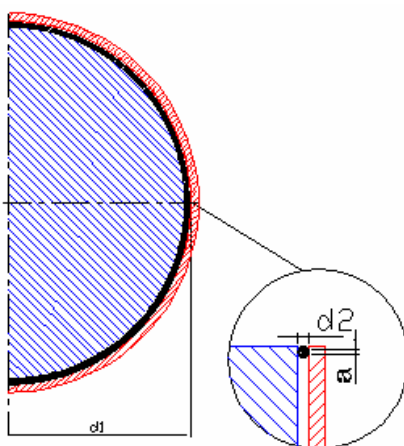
Dimensões do *o'ring* e superfície de contacto
